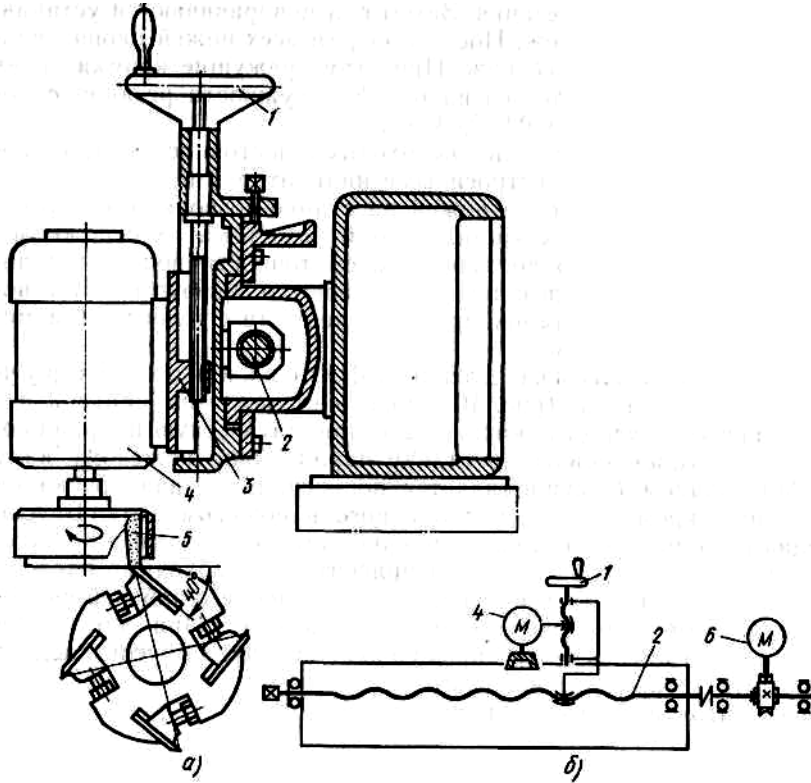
Приспособление с механическим приводом для заточки ножей в ножевом валу рейсмусового станка: а — общая схема, б — кинематическая схема; 1 — маховичок поперечной подачи, 2 — ходовой винт, 3 — суппорт, 4 — электродвигатель привода вращения заточного круга, 5 — заточный круг, 6 — электродвигатель привода продольной подачи
